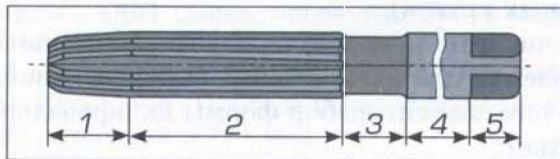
Развёртка с цилиндрическим хвостовиком: 1 – режущая часть, 2 – калибрующая часть, 3 – шейка инструмента, 4, 5 – хвостовик с квадратным концом
